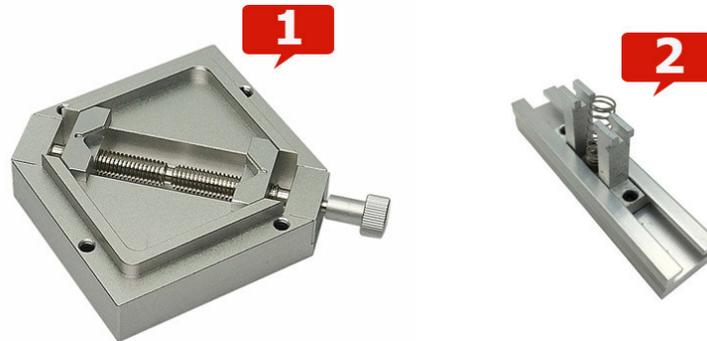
suporte BGA Honton Ht 90x90 (1) e suporte universal simples (2)
